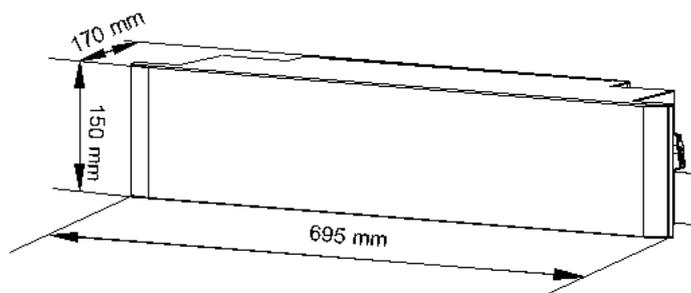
Dimensiones de la caja de conexiones para baterías BC3
